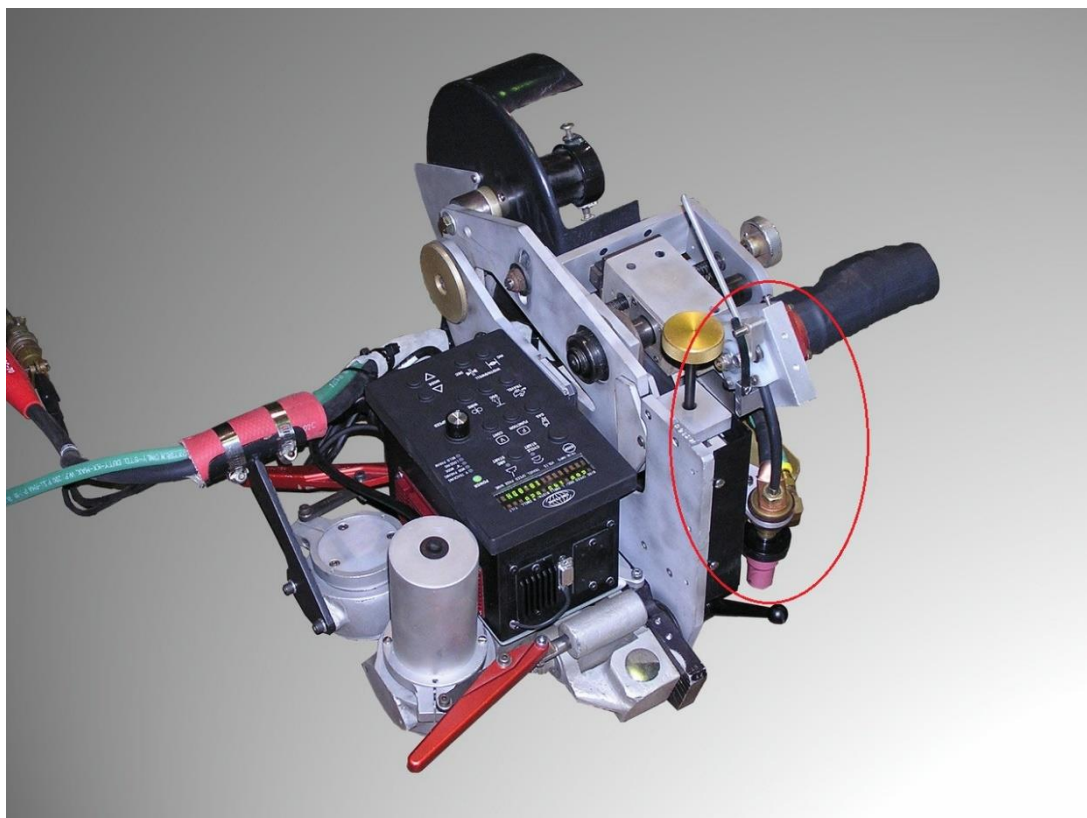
сварочная головка М-300 для сварки неповоротных стыков магистральных трубопроводов.
